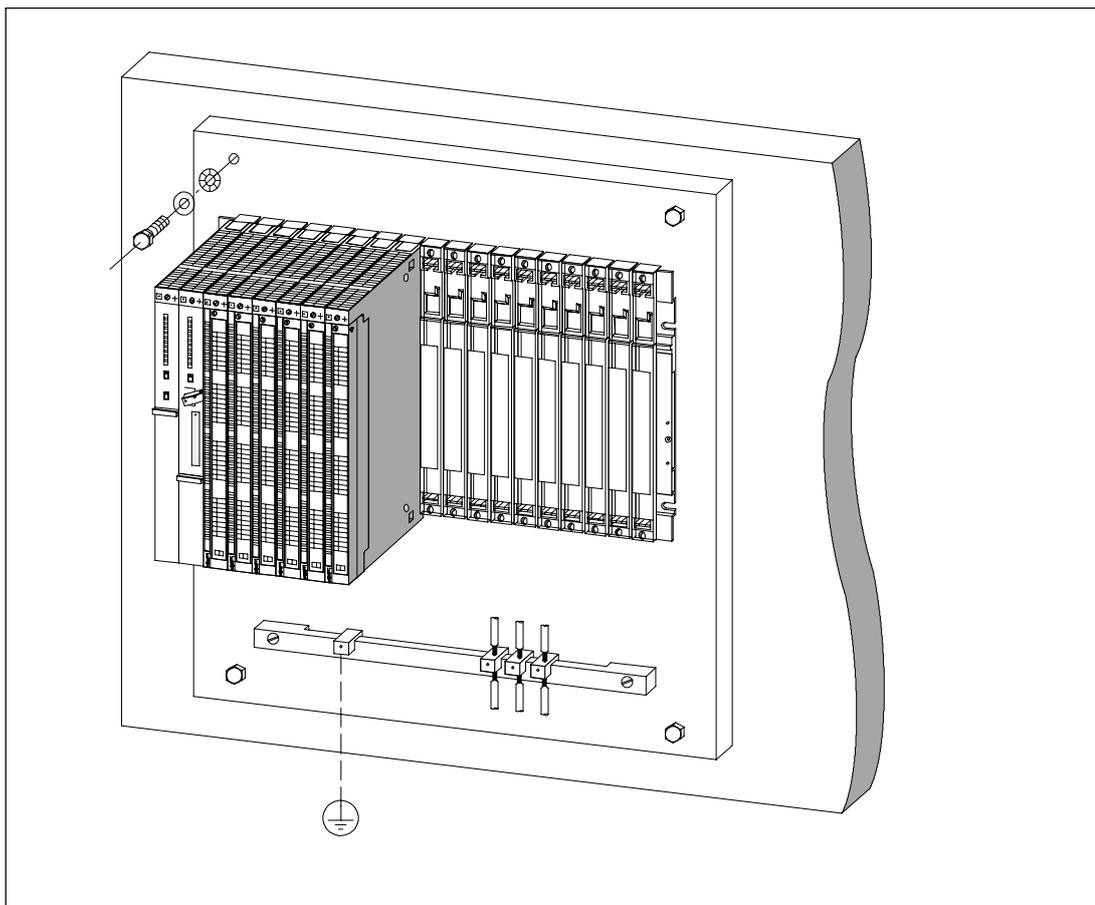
Montaggio corretto a parete di un S7-400 secondo le direttive EMC
